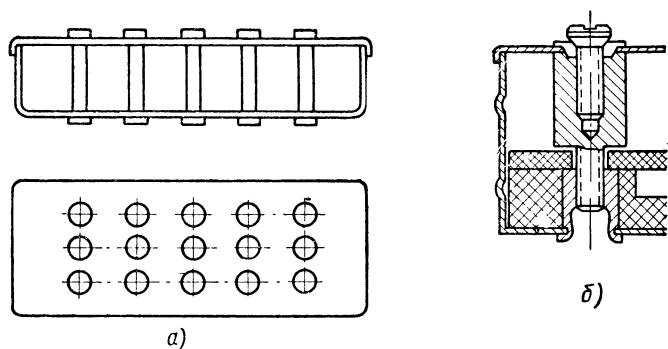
Коробчатая конструкция корпуса приемника с перемычками между стенками (а) и конструкция перемычки (б).
